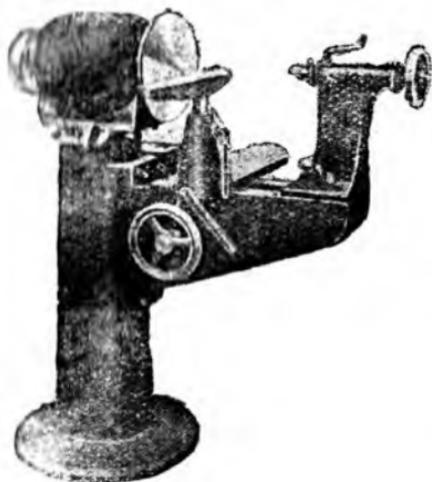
Лобовой токарный станок с съемкой и подвижной бабкой
